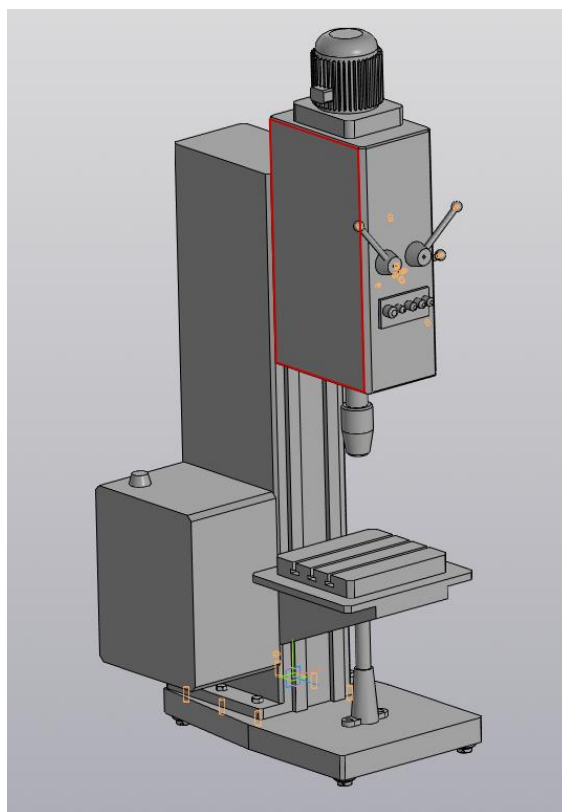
Загальний вигляд базової моделі верстата 2Н135
